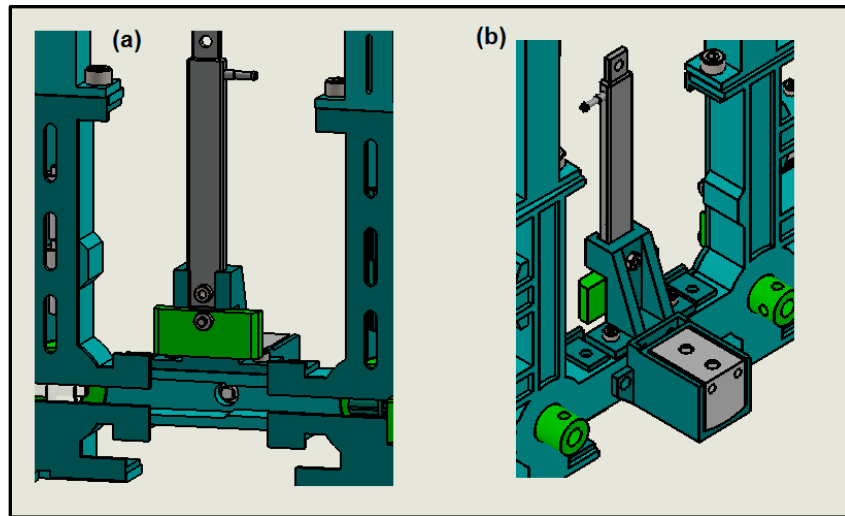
Montaje del módulo de expulsión (a) vista frontal; (b) vista trasera.
